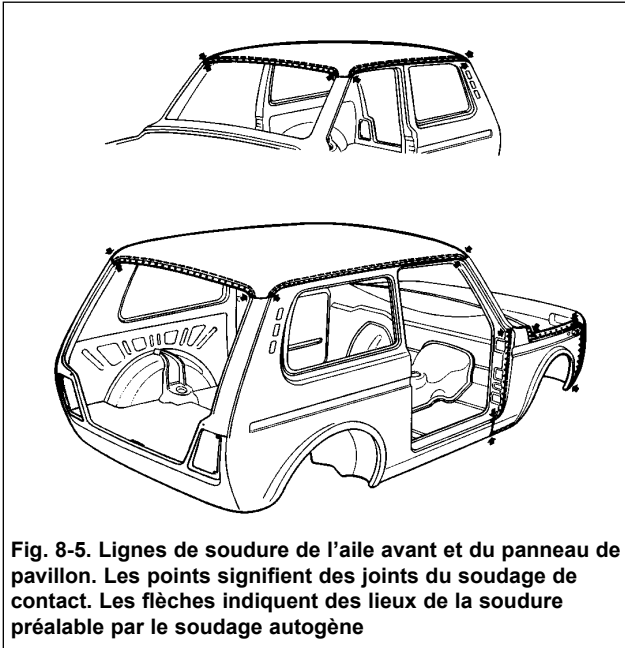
Lignes de soudure de l'aile avant et du panneau de pavillon. Les points signifient des joints du soudage de contact. Les flèches indiquent des lieux de la soudure préalable par le soudage autogène
